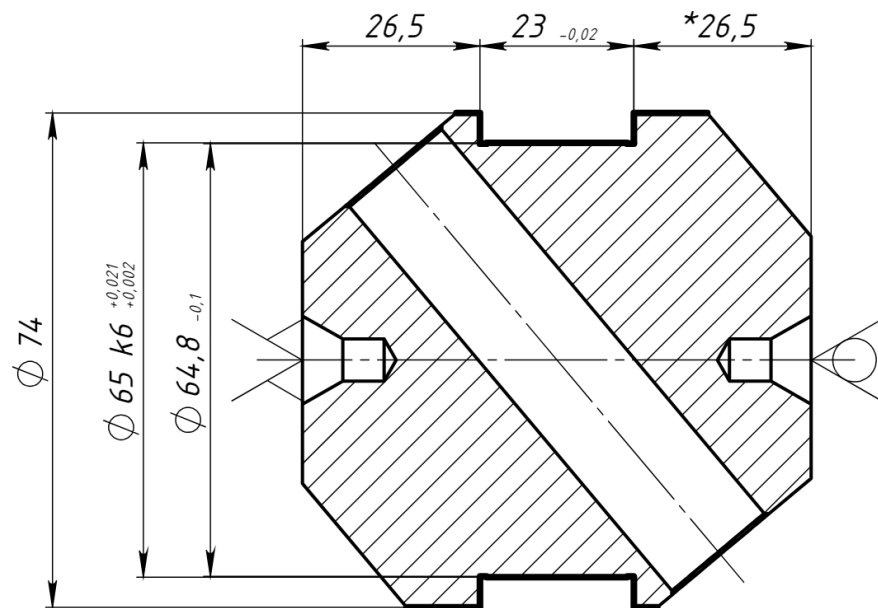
Схема встановлення та оброблення заготовки
